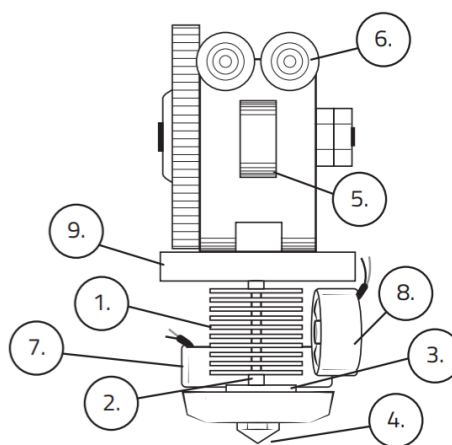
Estructura del extrusor y el cabezal de la impresora BCN3D+.
